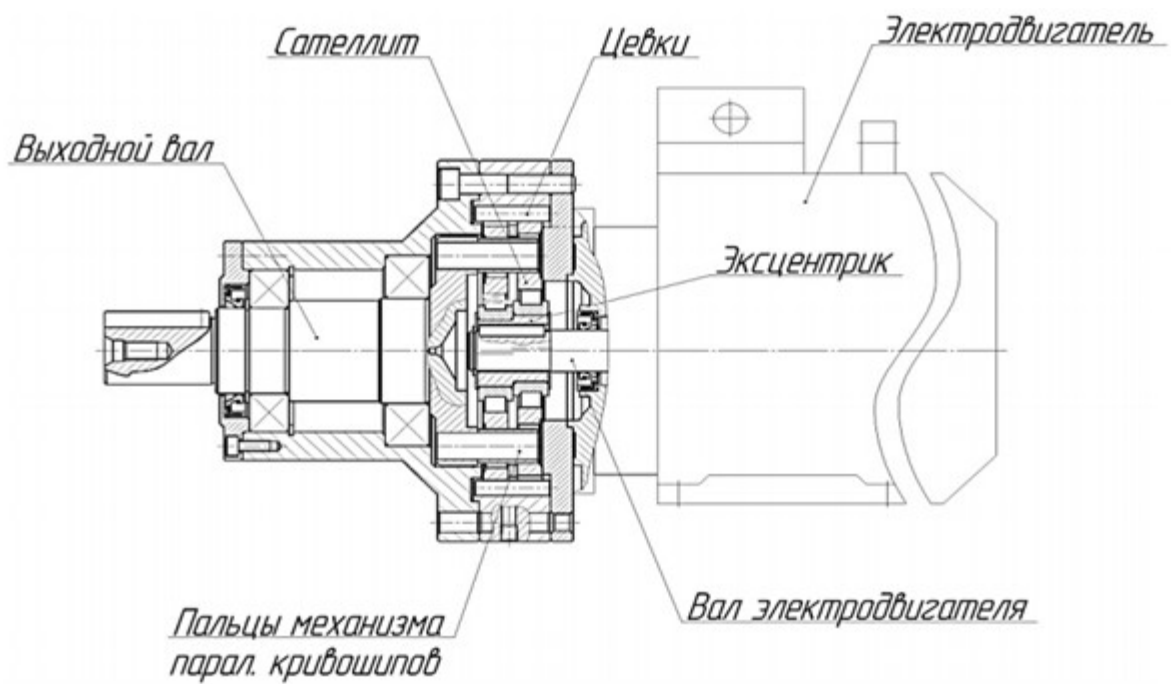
Планетарно-цевочный редуктор в сборе с двигателем
